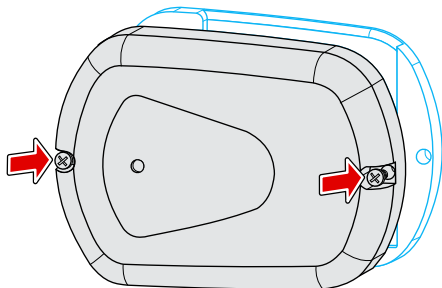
а – Установка держателя устройства «АвтоГРАФ-CardReader-Light/Light+».
